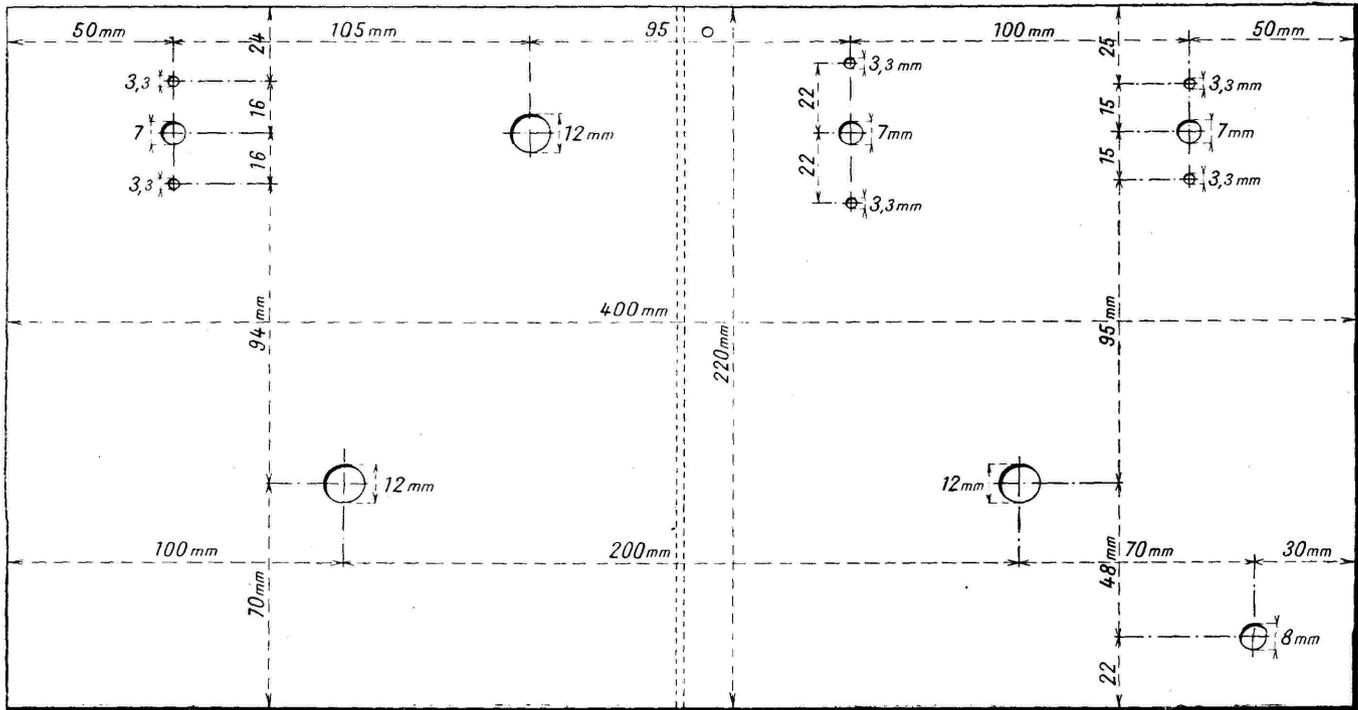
Plan de perçage du panneau de face en aluminium.
